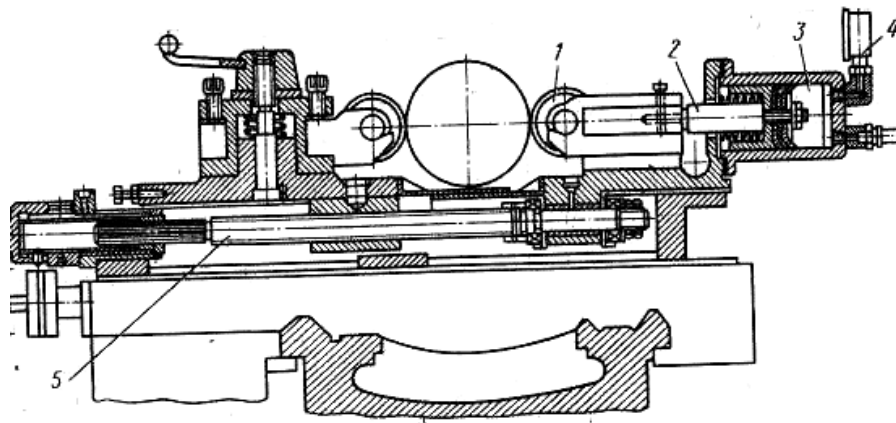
Пристрій з двома роликами для формоутворення зовнішніх канавок з радіусними поверхнями на токарному верстаті [21]
